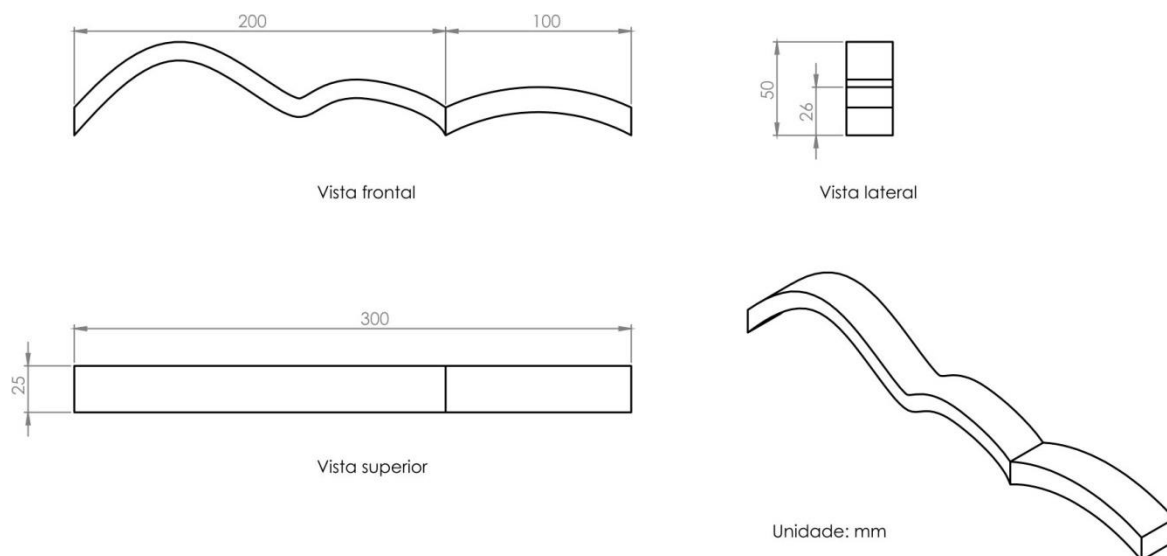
Desenho técnico com as dimensões gerais do multimódulo 1.
